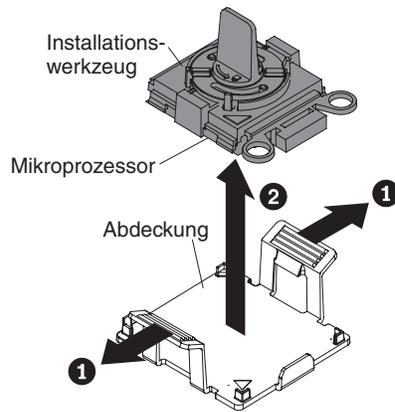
Abdeckung am Installationswerkzeug entfernen
